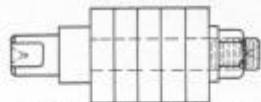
Mandril de tuercas para el acabado de discos para engranajes
